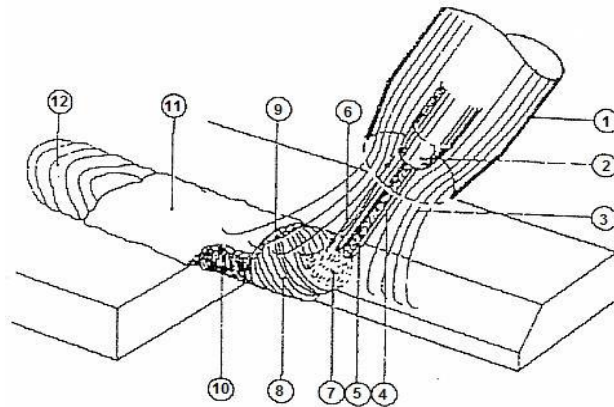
Proceso de soldadura MIG-MAG.
